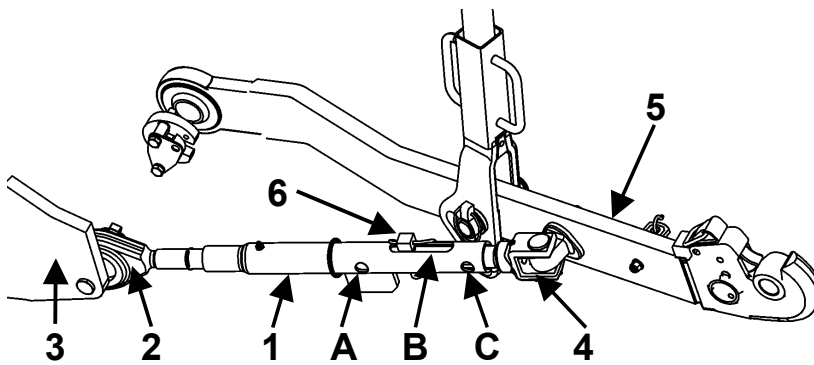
Teleskopbegrenzer der unteren Zugstangen. 1- Hülse; 2- Kugelendstück; 3- Befestigungskonsole; 4- Gabelendstück; 5- untere Zugstange; 6- Sperrsplint
